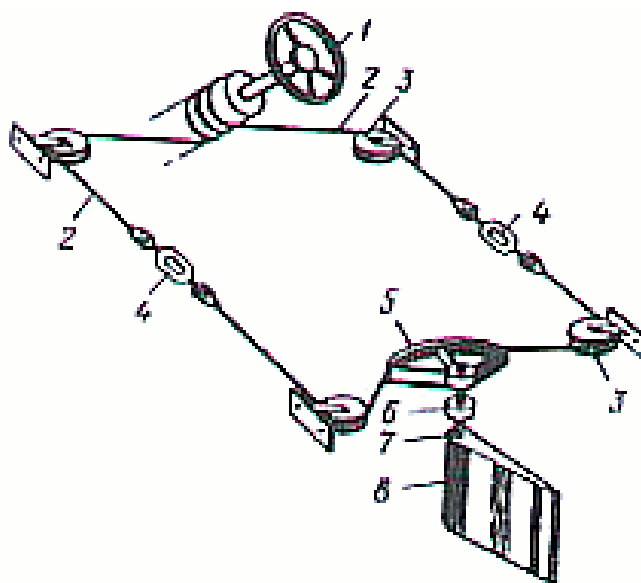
Схема рулевого устройства: 1 – штурвал; 2 – штуртрос; 3 – направляющие блоки; 4 – натяжные талрепы; 5 – румпель секторного типа; 6 – опорный подшипник; 7 – баллер; 8 – перо руля
